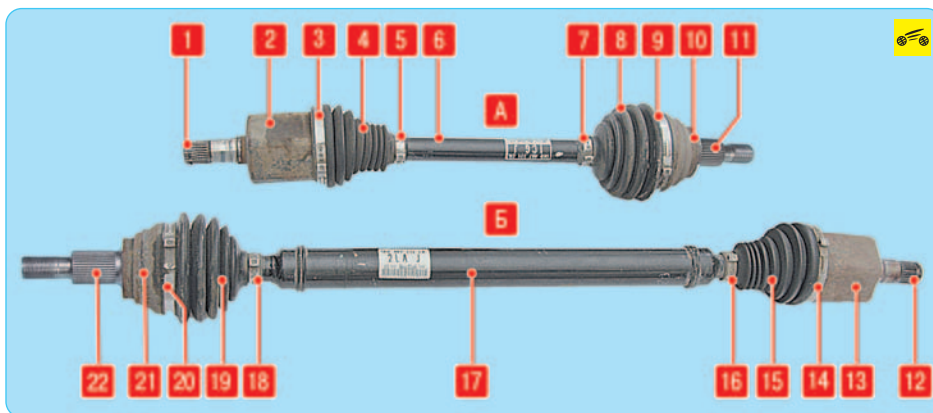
Приводы передних колес автомобиля с автоматической коробкой передач: А – привод левого переднего колеса; Б – привод правого переднего колеса; 1, 12 – стопорные кольца; 2, 13 – внутренние шарниры равных угловых скоростей; 3, 9, 14, 20 – большие хомуты крепления защитных чехлов шарниров; 4, 8, 15, 19 – защитные чехлы шарниров; 5, 7, 16, 18 – малые хомуты крепления защитных чехлов шарниров; 6, 17 – валы приводов; 10, 21 – наружные шарниры равных угловых скоростей; 11, 22 – шлицевые наконечники наружных шарниров
